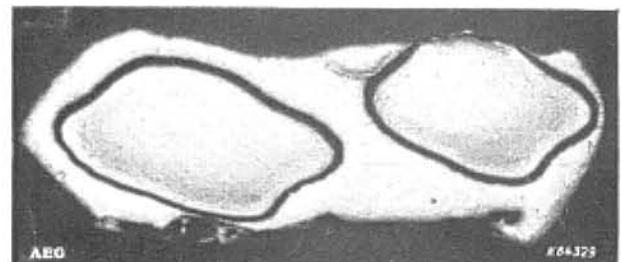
Schnitt durch Kreuz-Schweißung von kupferplattierten Nahtdrähten.
